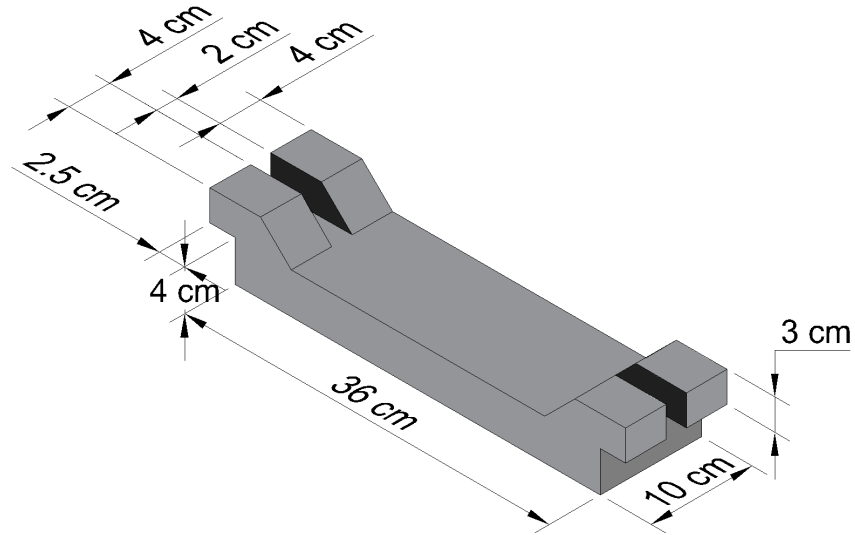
Detalle de la Bandeja Estructural Ranurada.
